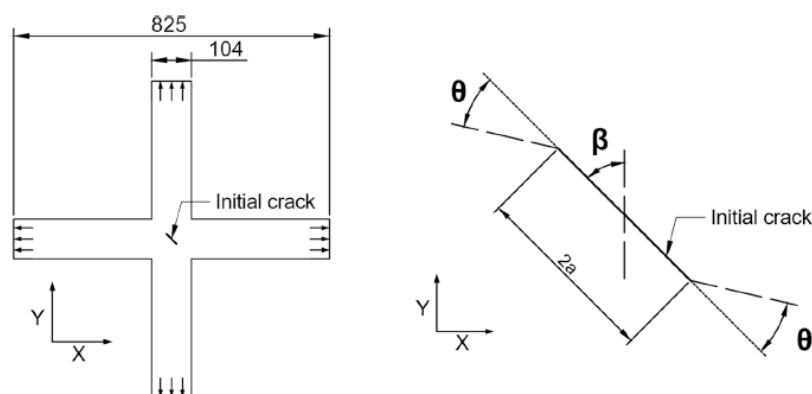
(esquerda) Geometria e dimensões do provete cruciforme [30];
